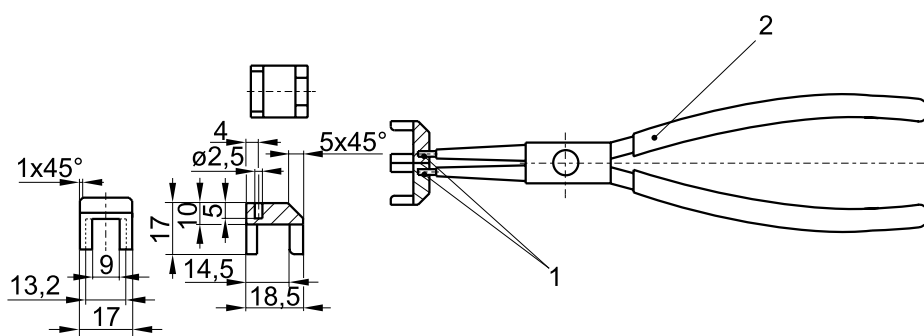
Werkzeug zum Einstecken der Kabelstecker für den Temperatursensor an den Kabelbaum
